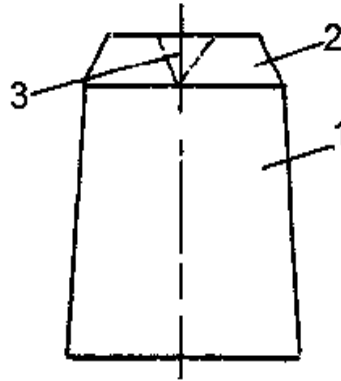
Форма зливка: 1 – зливоч; 2 – конусність; 3 – усадочна рихлість
